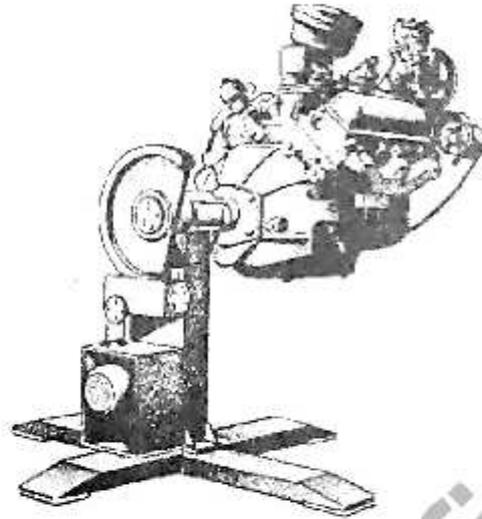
Стенд ОПТ-5557-ГОСПИТИ для разборки и сборки двигателей
